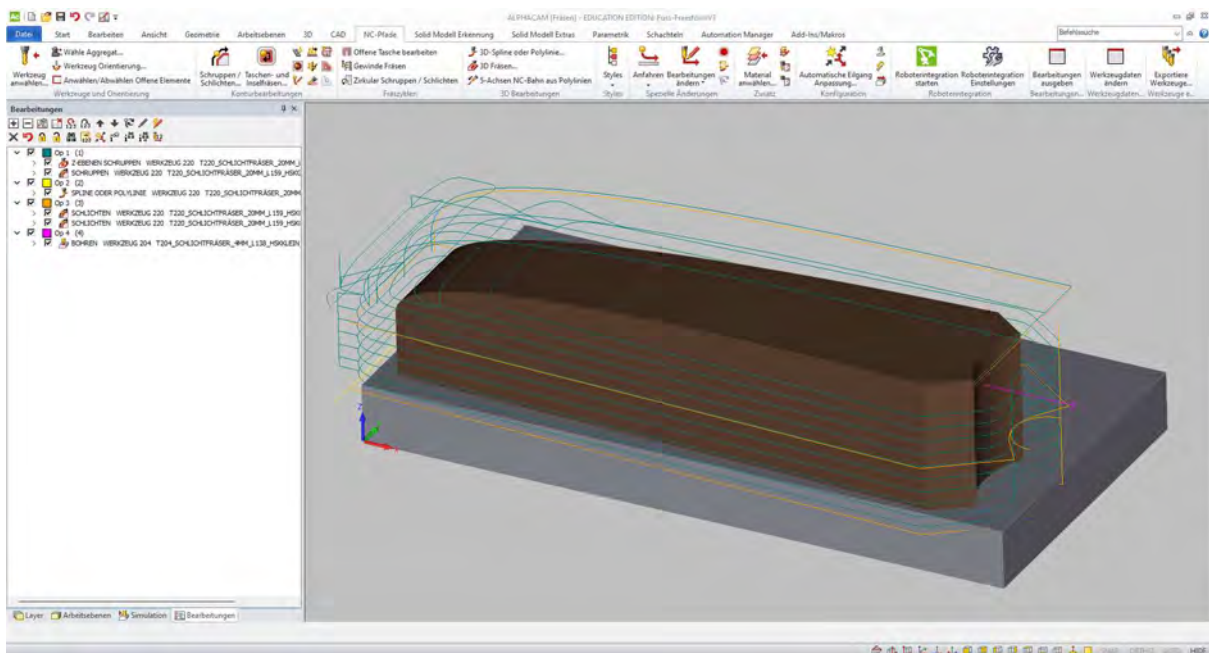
Fräsprogramm - Fuß Bearbeitung 1
